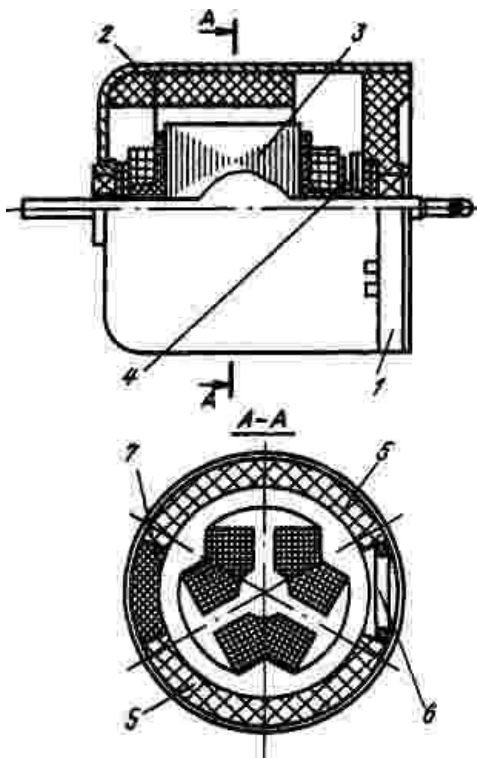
Мікродвигун з тризубцевим якорем: 1 - щит, 2 - корпус; 3 - якір; 4-колектор, 5 - постійні магніти; 6 - скоба, 7 – прокладка.
